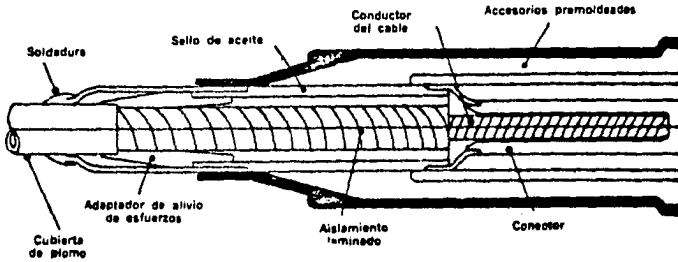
Empalme premoldeado para cable con aislamiento laminado.
